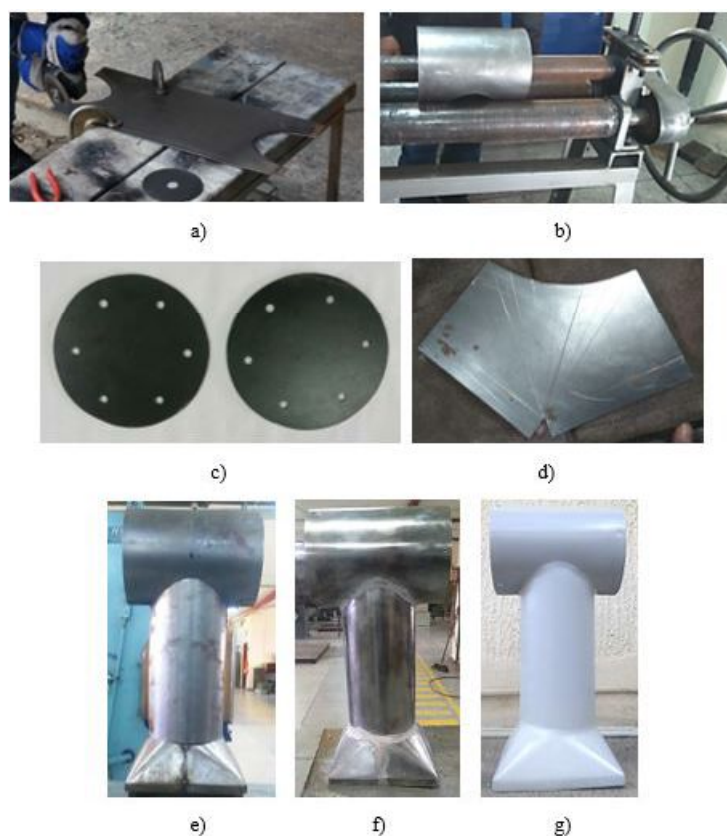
Procesos de a) corte b) rolado c) perforación d) trazado y doblado e) soldadura f) masillado g) pintura
